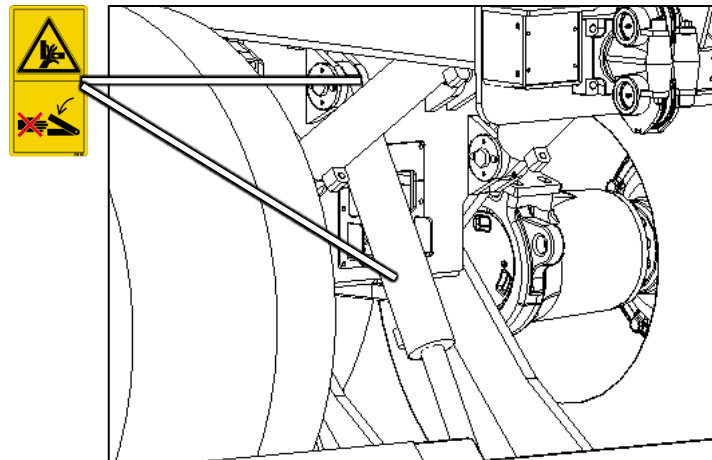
Zylinder für Seilrollenträger und Heckschild
